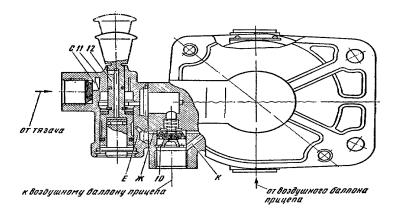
Воздухораспределитель: 1 — шток; 2, 5 — поршни; 3, 6 — крышки; 4 — корпус; 7 — тарелка штока; 8 — седло клапана; 9 — клапан перепускной; 10 — клапан обратный; 11 — кран растормаживания; 12 — шток крана
